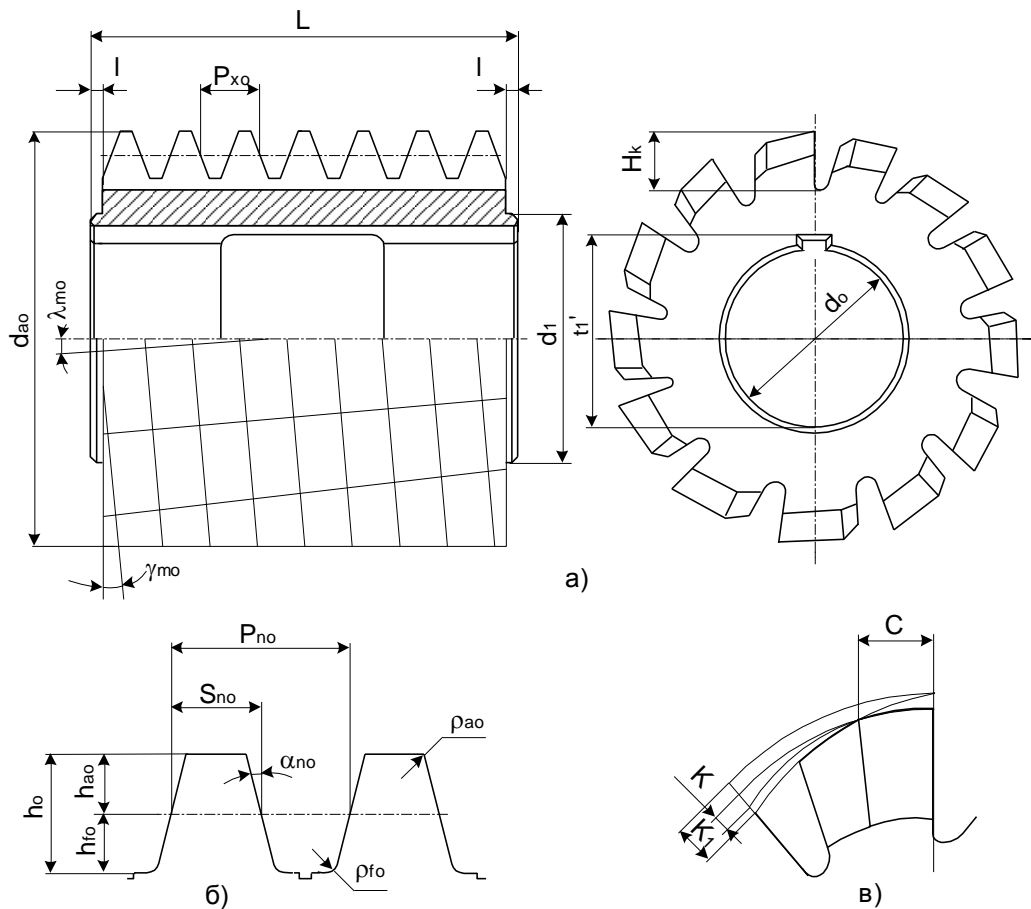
Червячная зуборезная фреза: а - общий вид; б - размер профиля в нормальном сечении; в - элементы затылования зубьев
